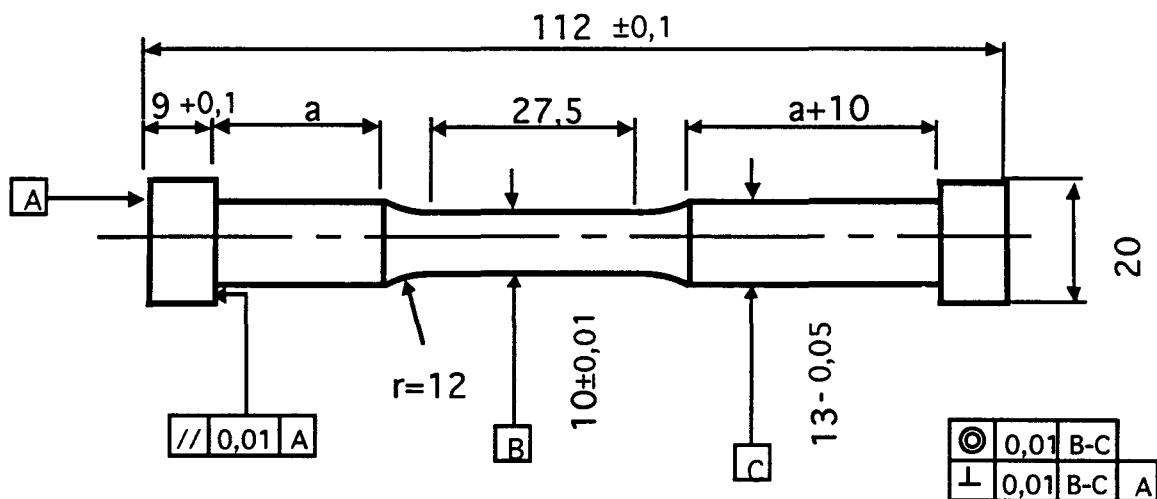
Dimensions des éprouvettes de fatigue et de traction monotone.
